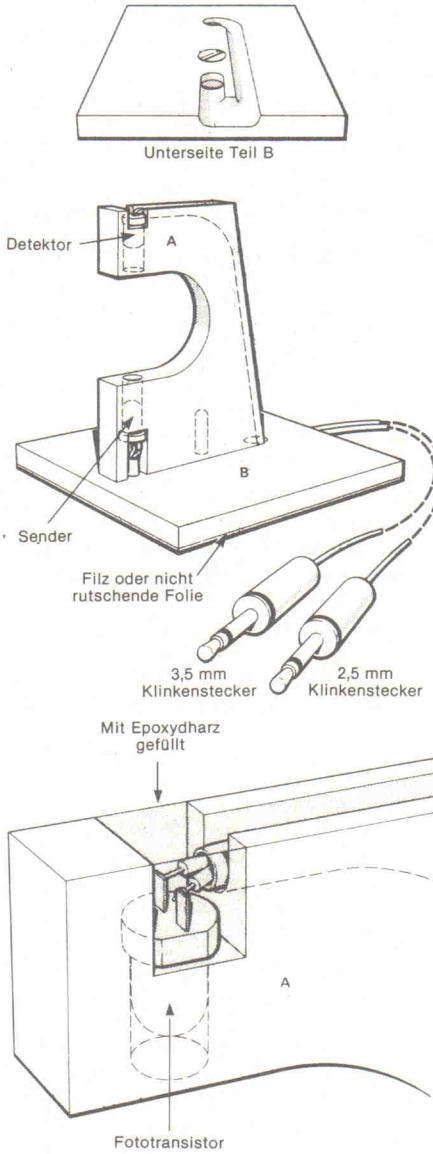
Konstruktionsdetails des Sensors. Für die Anschlußleitungen sollten verschiedene große Stecker verwendet werden, um Verwechslungen auszuschließen.
